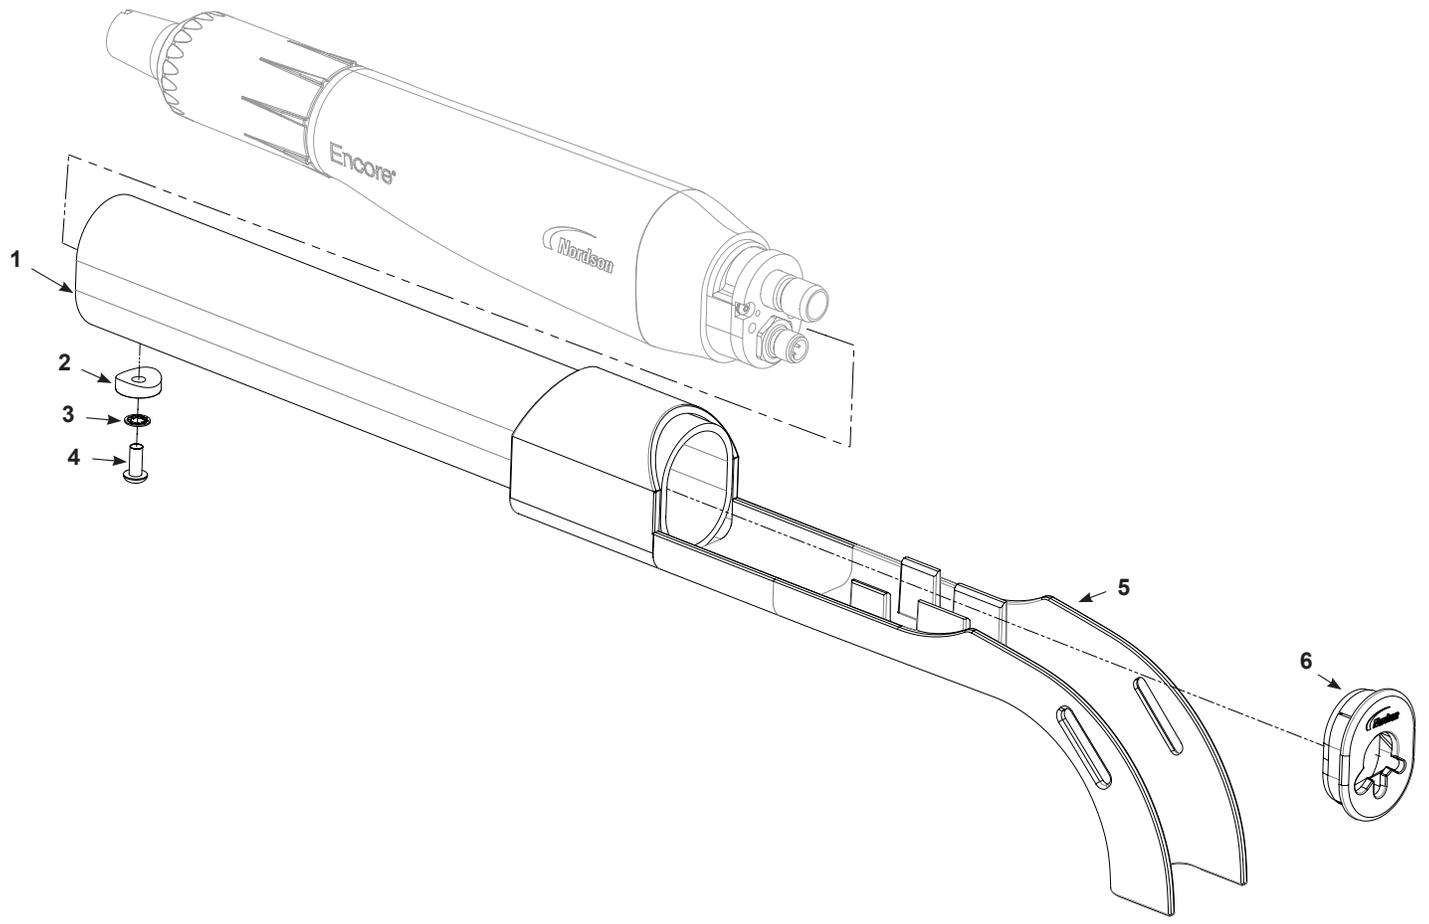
Piezas de una pistola de aplicación de montaje en tubo
